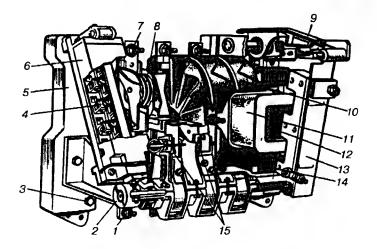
Контактор переменного тока с поворотной магнитной системой и валом:
